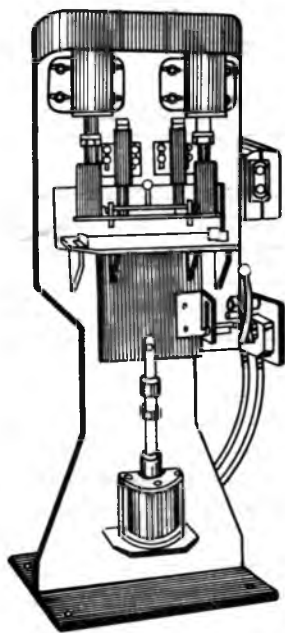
Вертикально-сверлильный двухшпиндельный полуавтоматический станок
